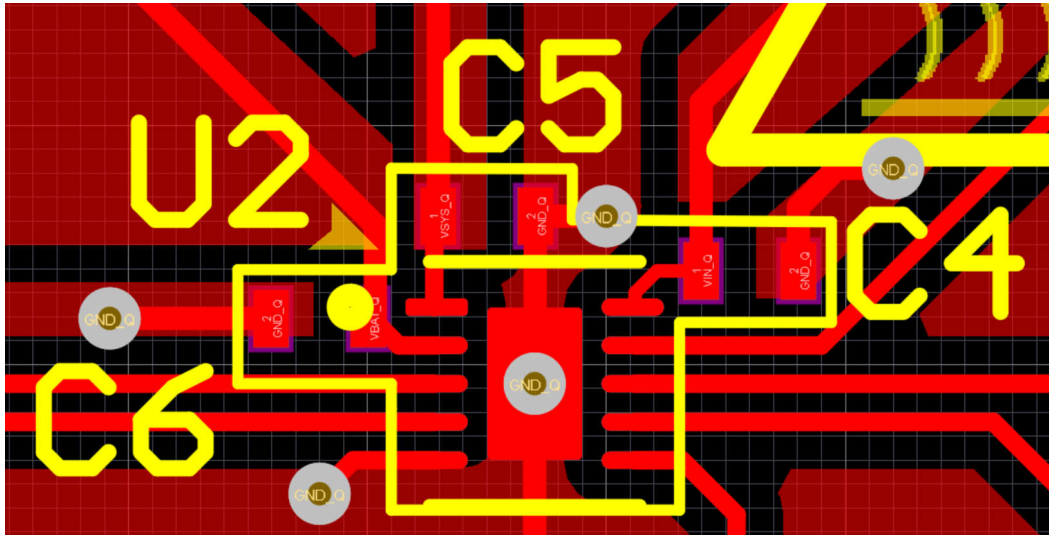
BQ25181 扇出，焊盘上走线为 8mil
